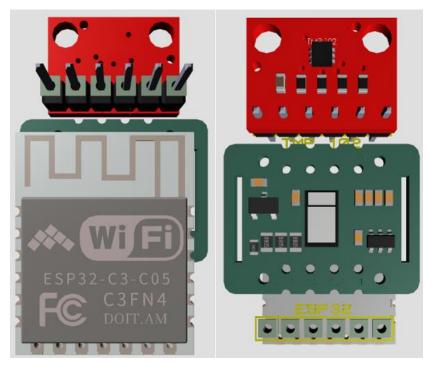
Modelo 3D de PCB Elaborado por: El investigador
